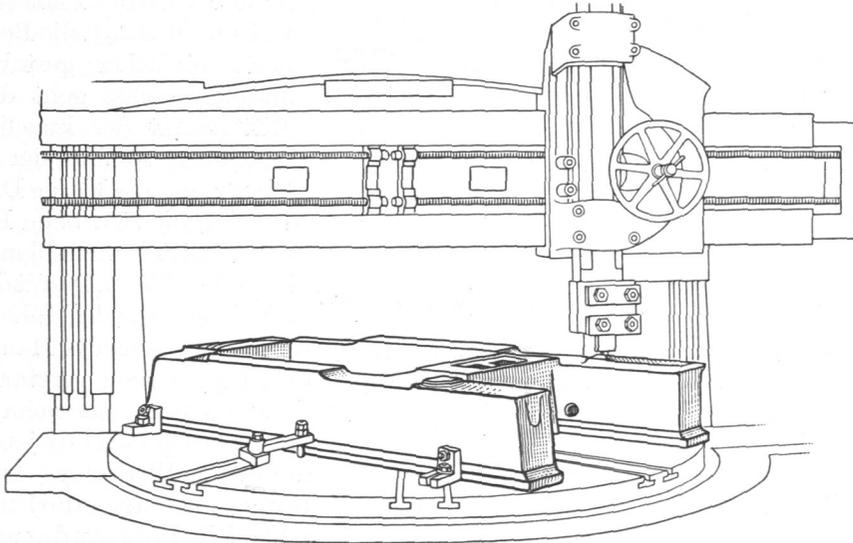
Gleich hohe Lage der Arbeitsflächen an einem Rahmen, zwecks gleichzeitiger Bearbeitung. (A. E. G. Berlin).
